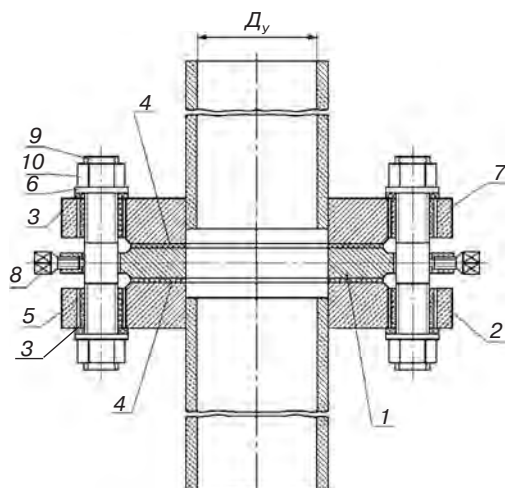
Изолирующее фланцевое соединение: 1, 2, 7 — фланцы; 3, 4 — прокладки; 5 — втулка; 6 — шайба; 8 — винт; 9 — шпилька; 10 — гайка
